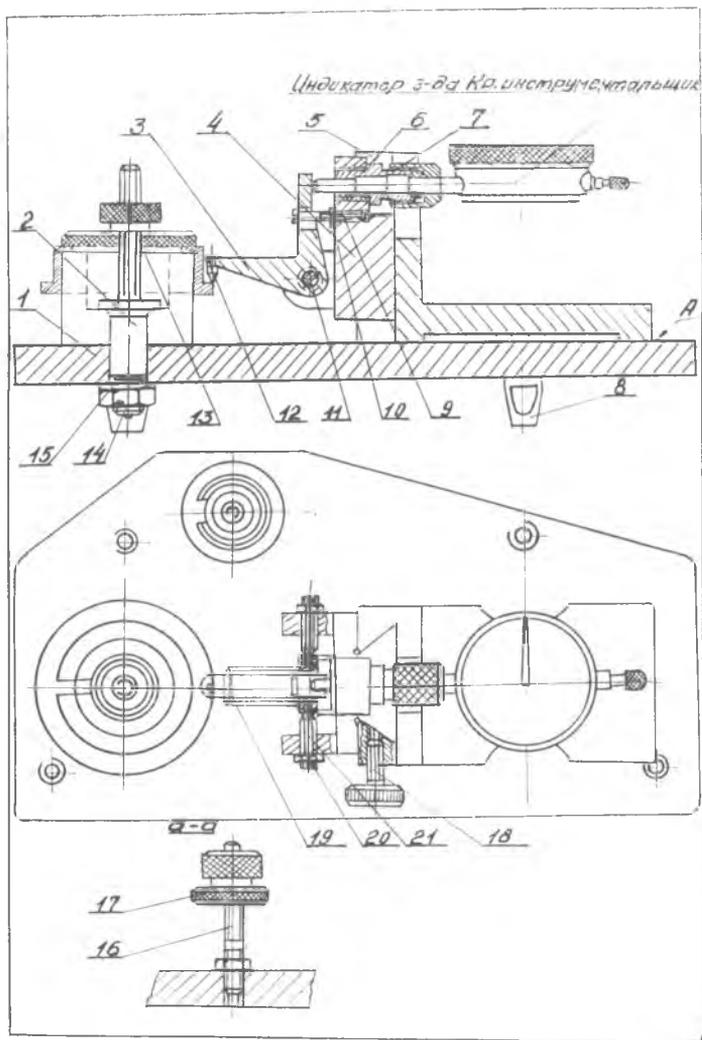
Универсальный прибор для контроля размера втулки: 1 — плита; 2 — палец; 3 — рычаг; 4 — ползу; 5 — стойка; 6 — вставка; 7 — зажим; 8 — ножка; 9, 18, 21 — винты; 10, 13, 14, 20 — гайки; 11 — ось; 12 — упор; 15 — шайба; 16 — шпилька; 17 — шайба; 19 — пружина
